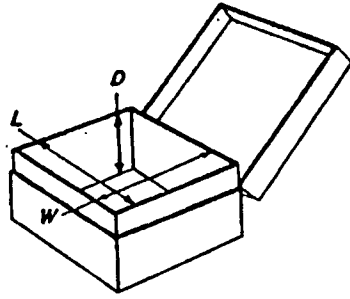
Flanged and shouldered box with flanged lift-off lid
